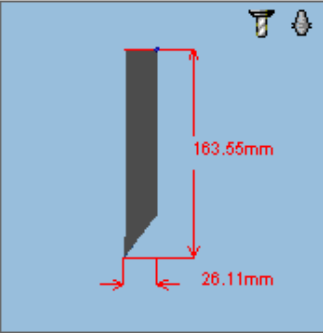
Державка різця «SVJBR 2525M 16»
